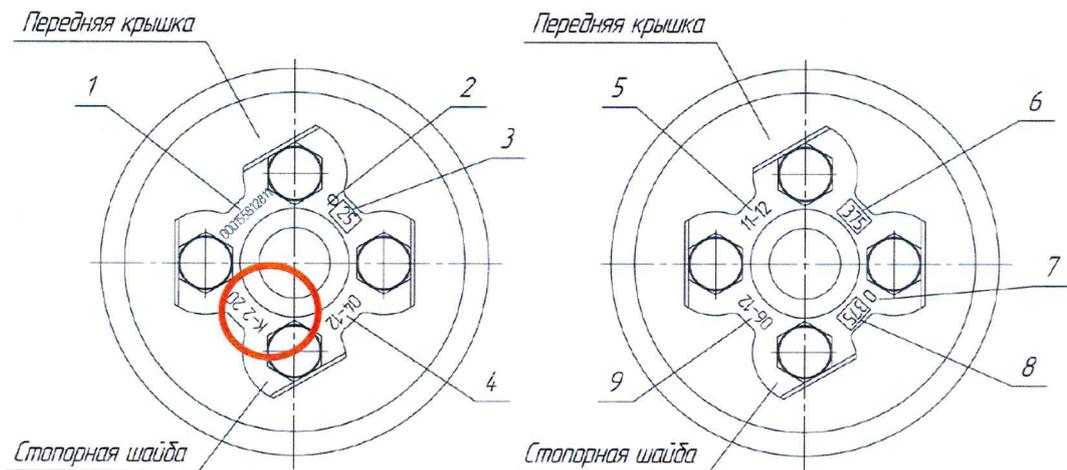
Внешний отличительный признак подшипников кассетного типа в габаритных размера 130x250x160 мм и 150x250x160 мм под адаптер для крепления четырьмя болтами М20
